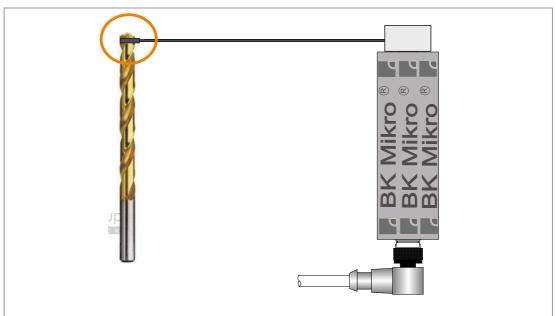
Ausrichten der Tastnadel für radiale Werkzeugabtastung
